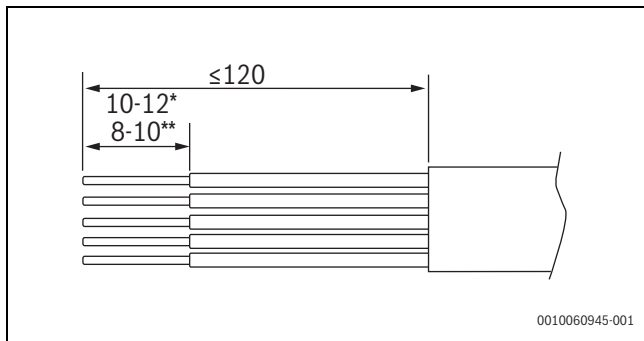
Dénudage des fils pour le raccordement secteur (mm)
